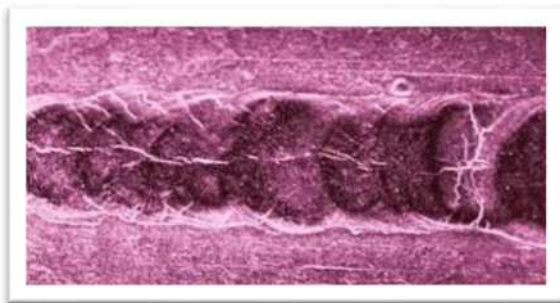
Fissuration à chaud. [10]
